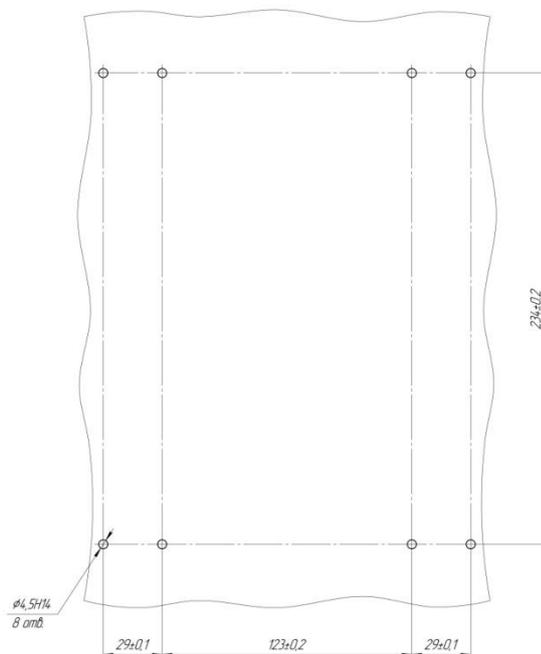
Габаритные и присоединительные размеры устройства РС830-ФКС-ЖД при внешнем монтаже, обеспечивающем его поворот вверх/вниз
